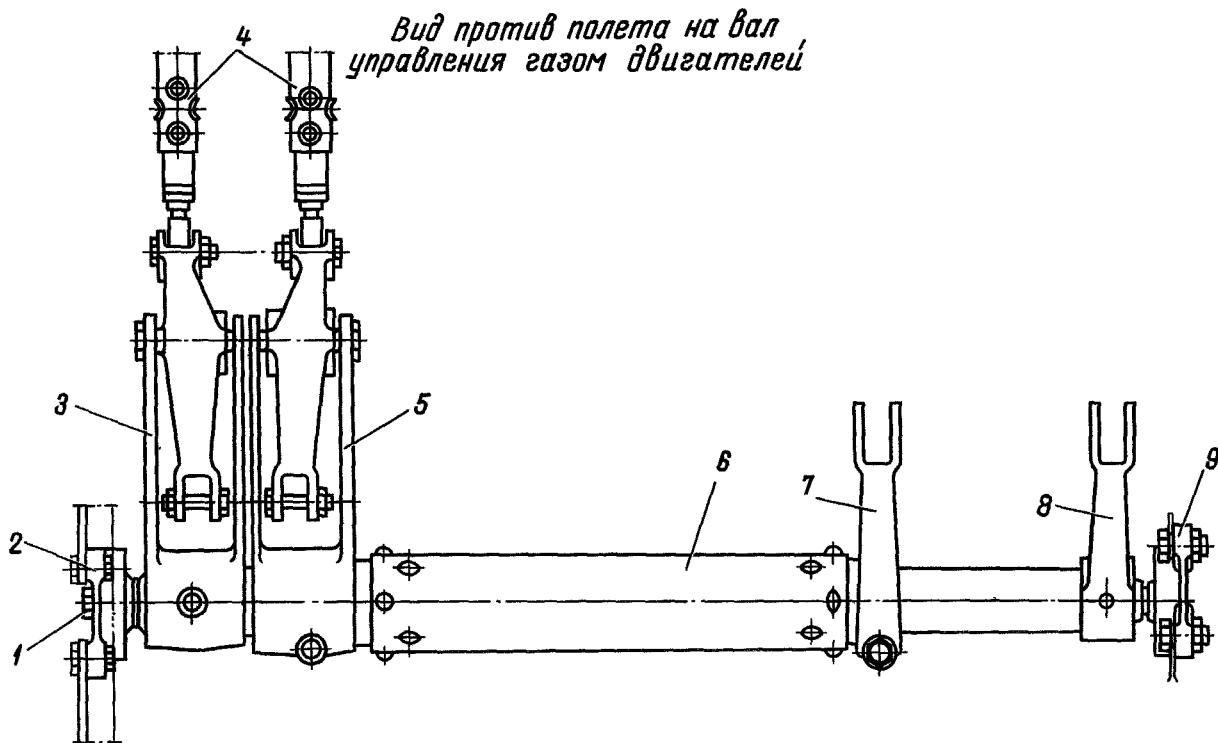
Вал управления газом двигателей (черт. 8А-5913-70);
